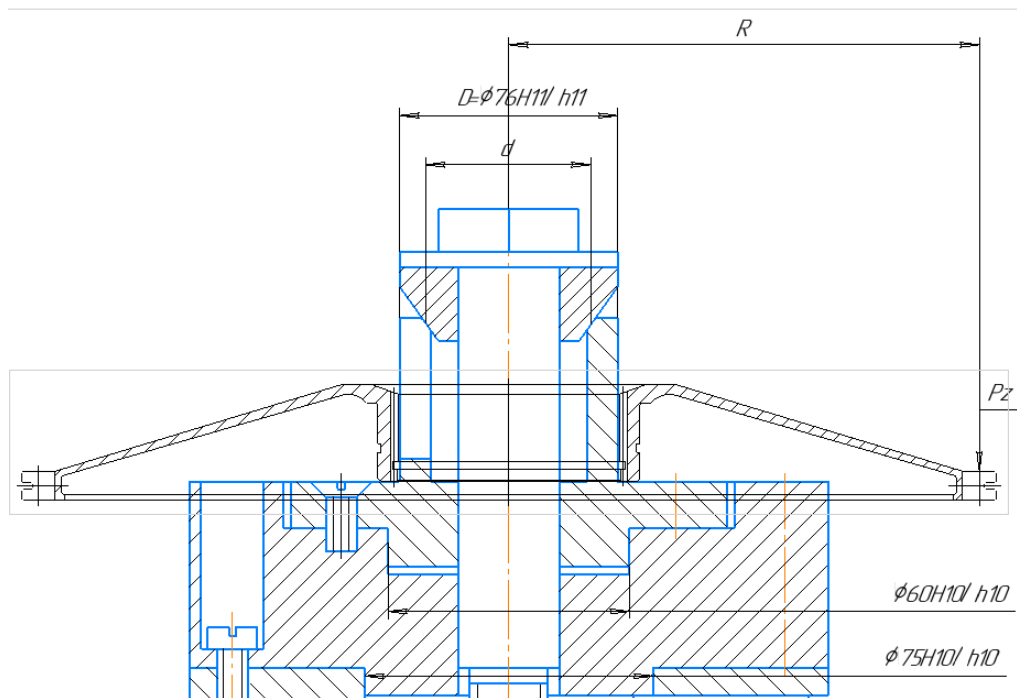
Конструктивна схема зубчастого фрезерного пристосування
